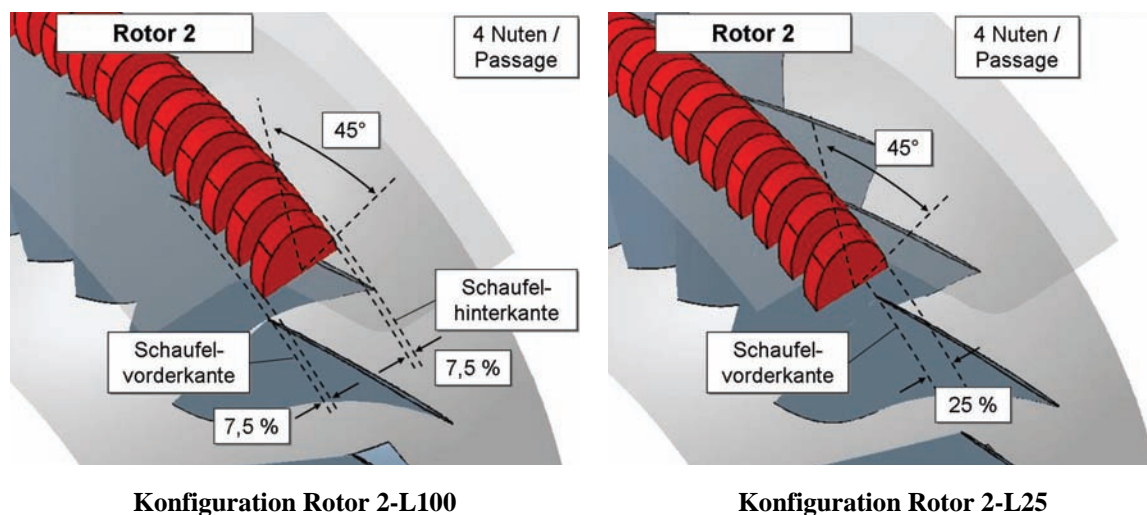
Untersuchte Axialnutenkonfigurationen am Rotor 2
